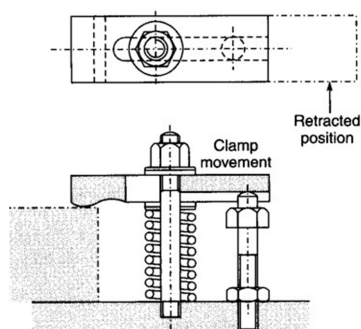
1 Klem Baut/Sekrup dan Mur
